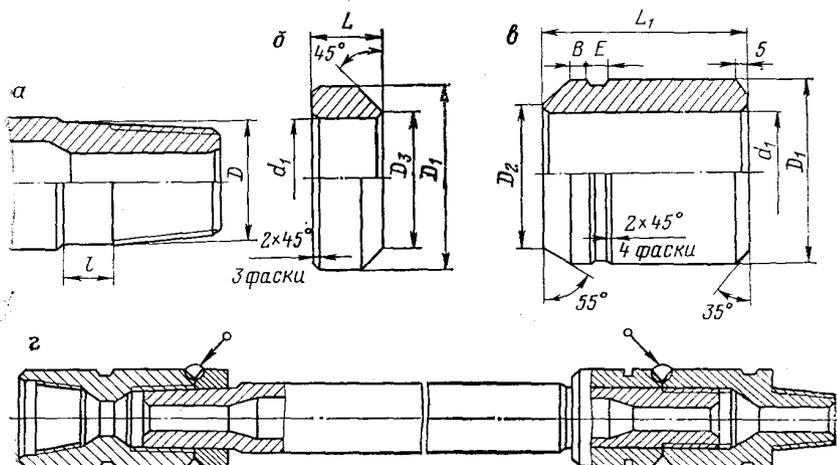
Схема установки и приварки стабилизирующих колец
